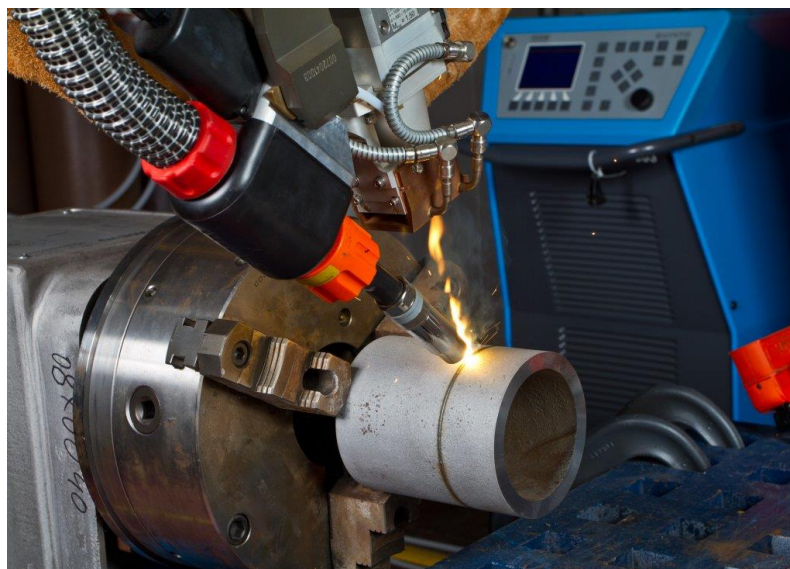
Сварка в среде углекислого газа
